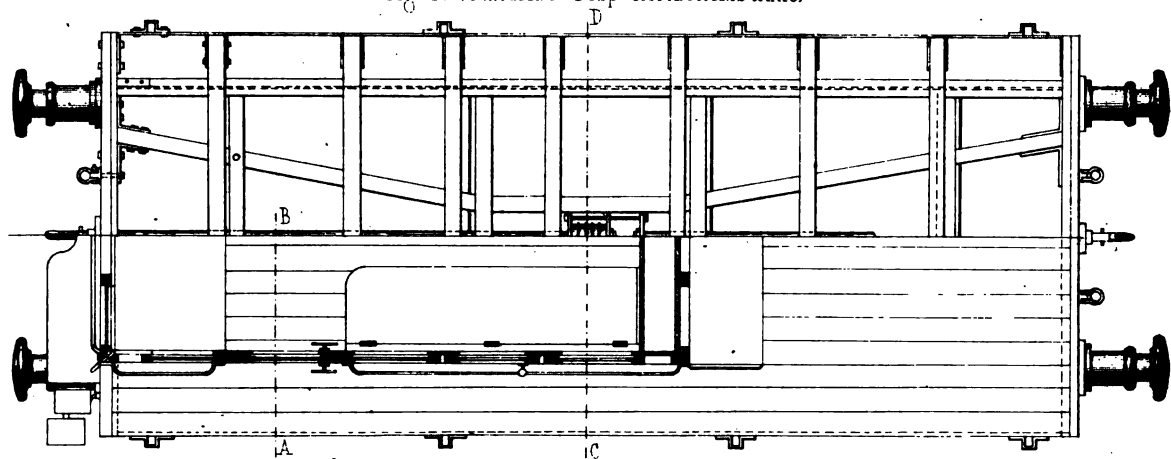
Grundriss resp Horizontalschnitt.
